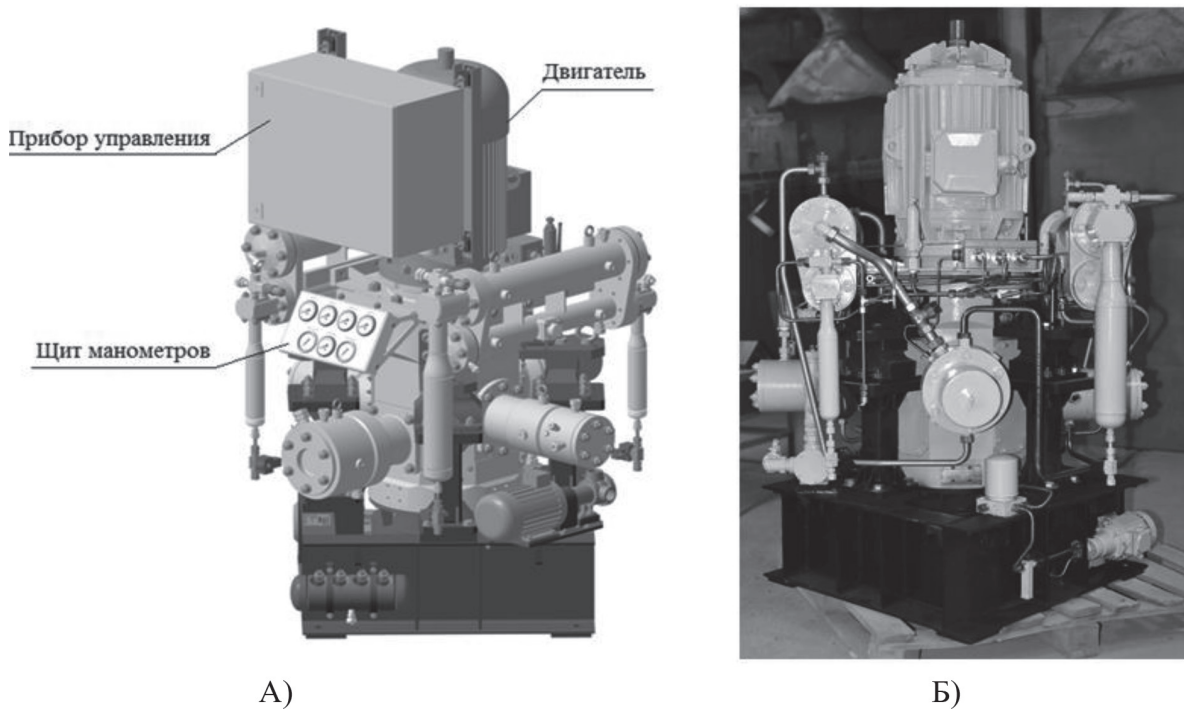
Компрессорная установка: А) 3D-модель; Б) фотография готовой установки
